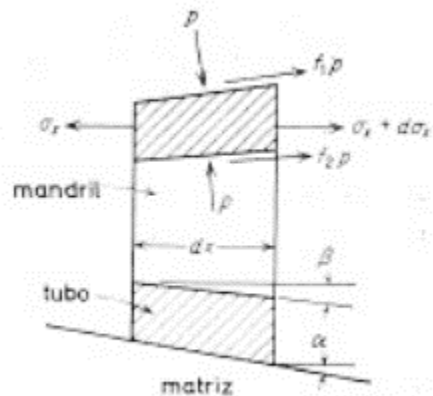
Tensiones sobre un elemento de tubo durante el trefilado con mandril fijo.
